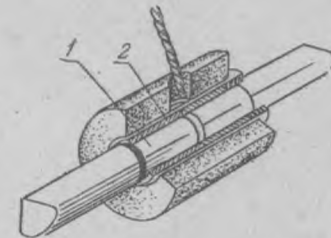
Термитная сварка алюминиевых жил встык
